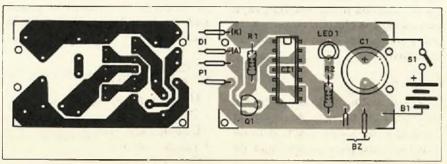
Placa de circuito impresso do teste de controles remotos.
